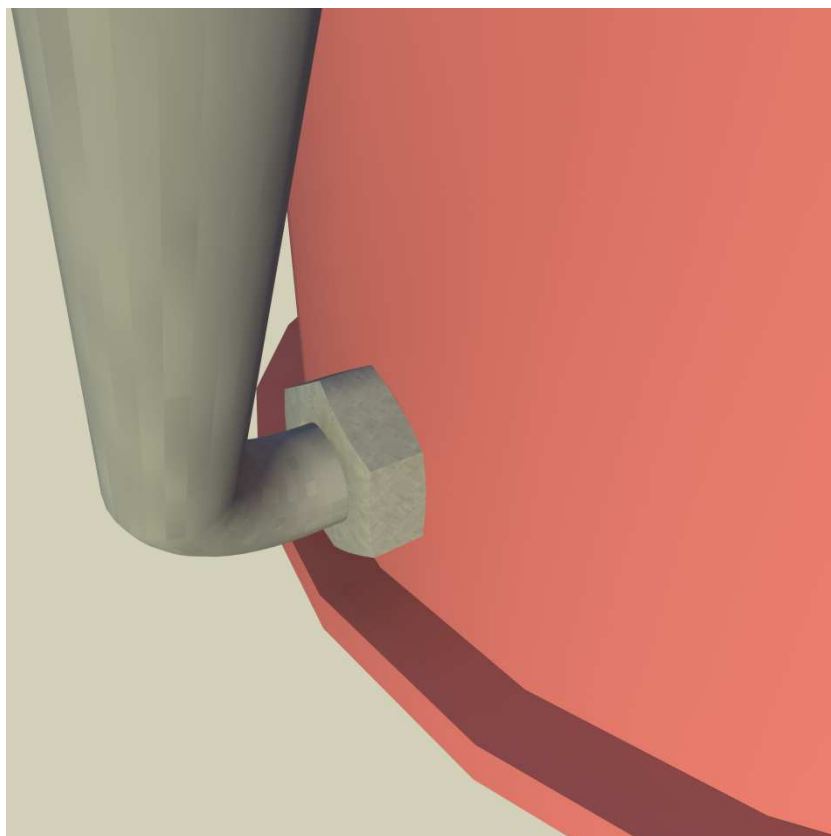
Piezometr, určený ke snadnému odečtu hladiny vody
